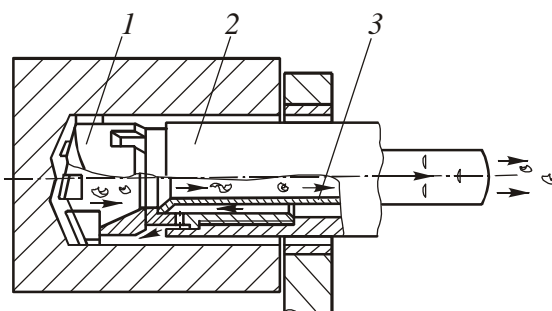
Схема обработки глубоких отверстий эжекторным сверлом:
